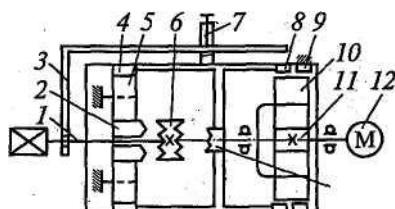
Кинематическая схема резьбонарезной машины
